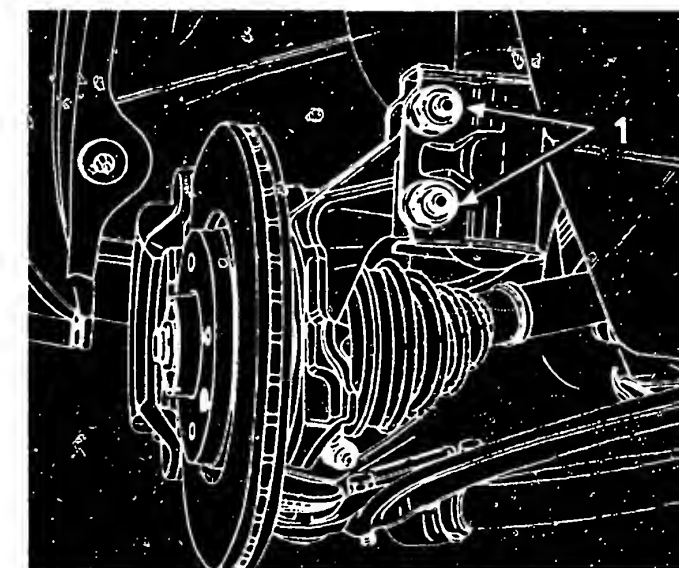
Bei den längs eingebauten Motoren sind die unteren zwei Schrauben (1) der Federbeinbefestigung mit einer Verzahnung versehen. Die Schrauben lassen sich nicht drehen und sind beim Ausbau mit einem Kunststoffhammer auszutreiben.
